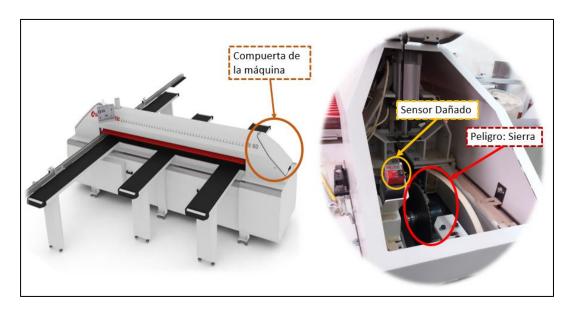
Ubicación del sensor dañado de la máquina cortadora de melamina
